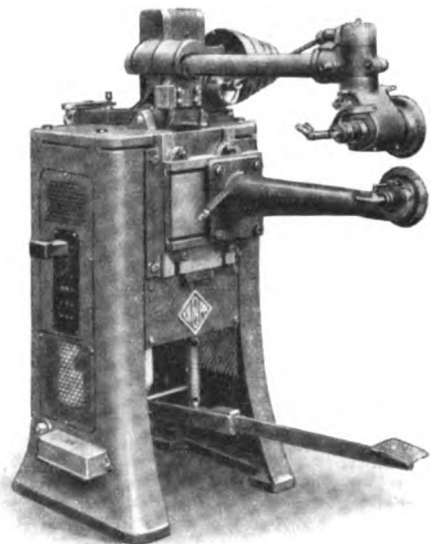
Nahtschweißmaschine „Lana/Runa“.
